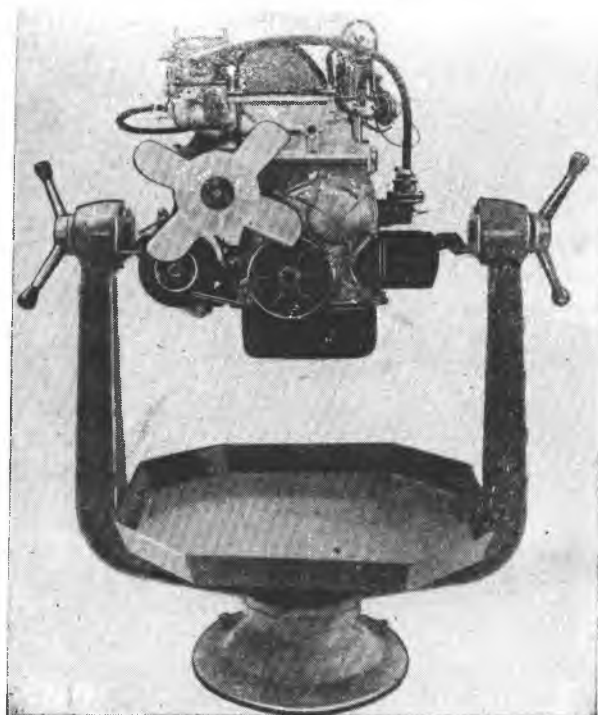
Стенд Ач.22204 для разборки и сборки двигателя
